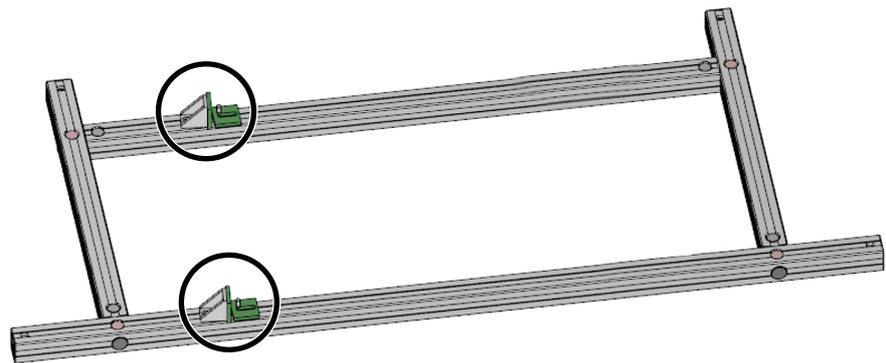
Linke Befestigungswinkel Schrauben lösen (Abbildung beispielhaft)
